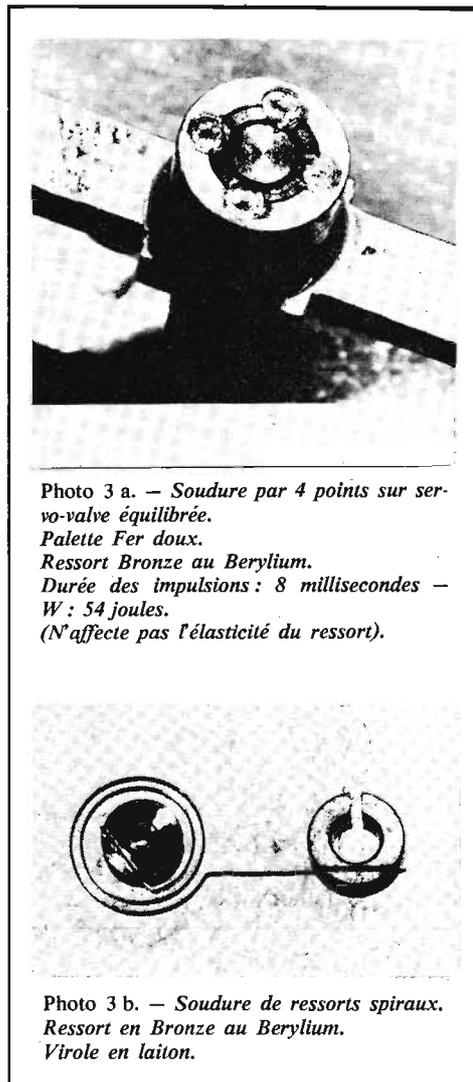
a. — Soudure par 4 points sur servo-valve équilibrée.
